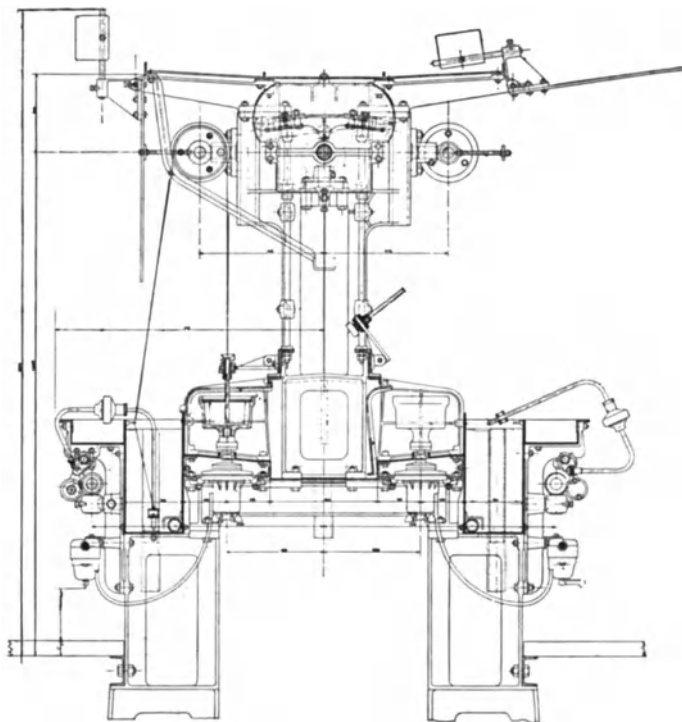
Topfspinnmaschine mit Schrumpfspinnapparatur und gleichgerichteten Maschinen- und Galettenachsen (Blaschke).
